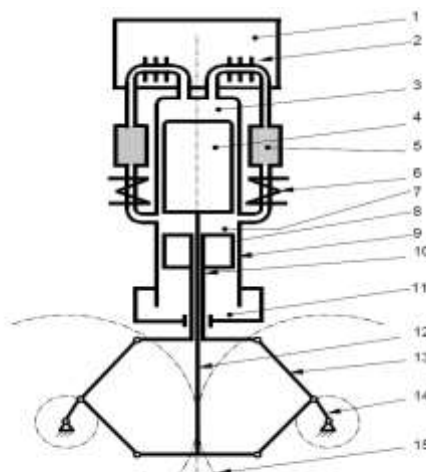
Schema constructivă a motorului Stirling Philips:
